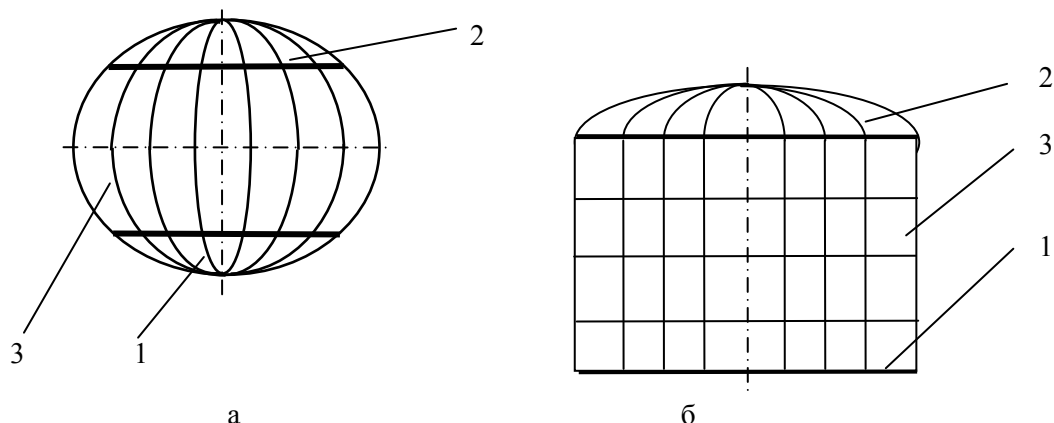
Типовые сооружения, изготавливаемые с использованием методов штамповки: сферический (а) и цилиндрический (б) резервуары: 1, 2 – нижнее и верхнее днище; 3 – пояс резервуара
